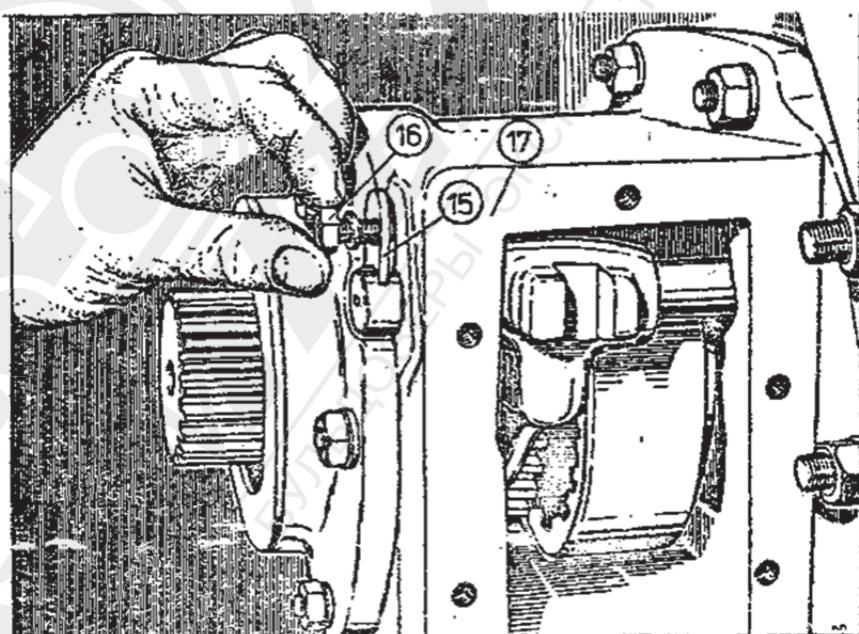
Крепление к корпусу 17 установочной плитки 15 с помощью винта M6 x 20 /16/.
